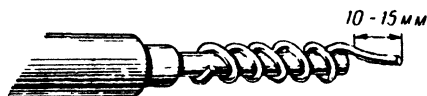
Дополнительное приспособление для пайки мелких деталей.
